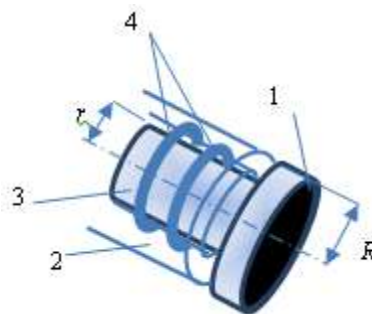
Конструкция вращающихся вокруг своего центра резцов типа PDC: 1 – резец PDC; 2 – корпус; 3 – ось; 4 – стопорные упругие кольца
